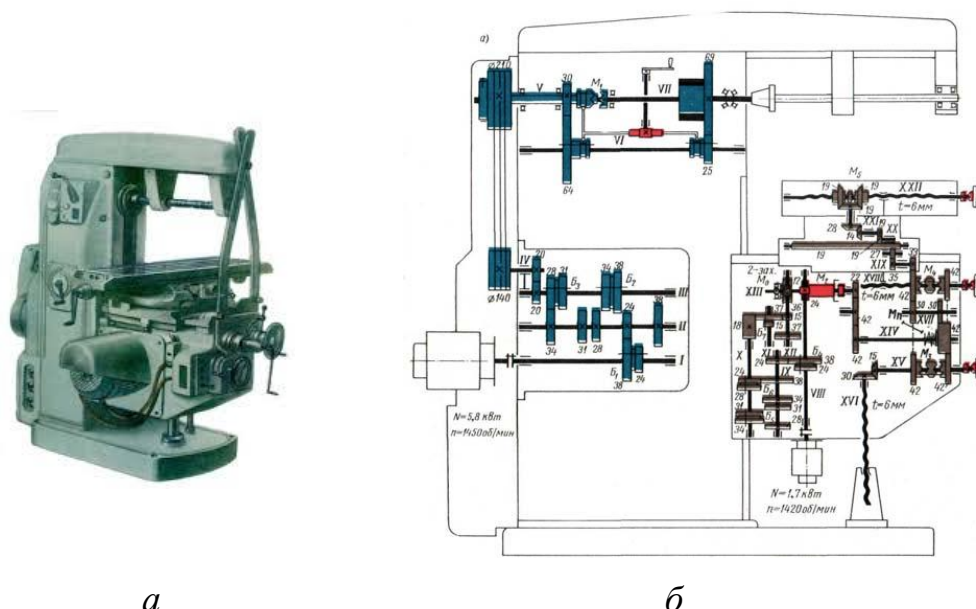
Горизонтально-фрезерный станок мод. 6N81Г (а) и его кинематическая схема (б)
